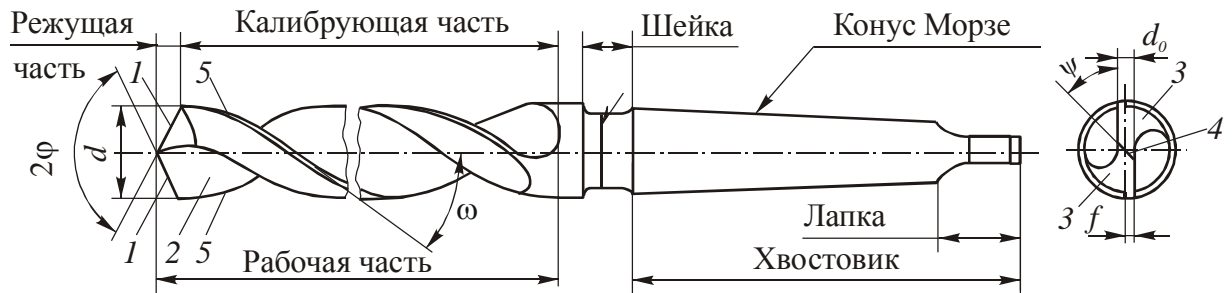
Основные конструктивные элементы и геометрические параметры спирального сверла: 1 – главная режущая кромка; 2 – передняя поверхность; 3 – главная задняя поверхность; 4 – поперечная режущая кромка; 5 – вспомогательная режущая кромка
